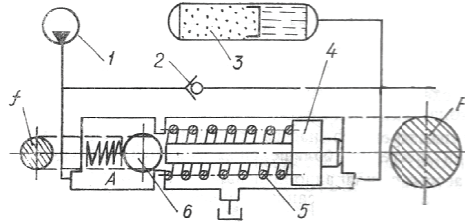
Схема АРН прямої дії: 1 – поршень; 2,6 – клапан; 3 – рухомий поршень; 4 – стержень; 5 – пружина
